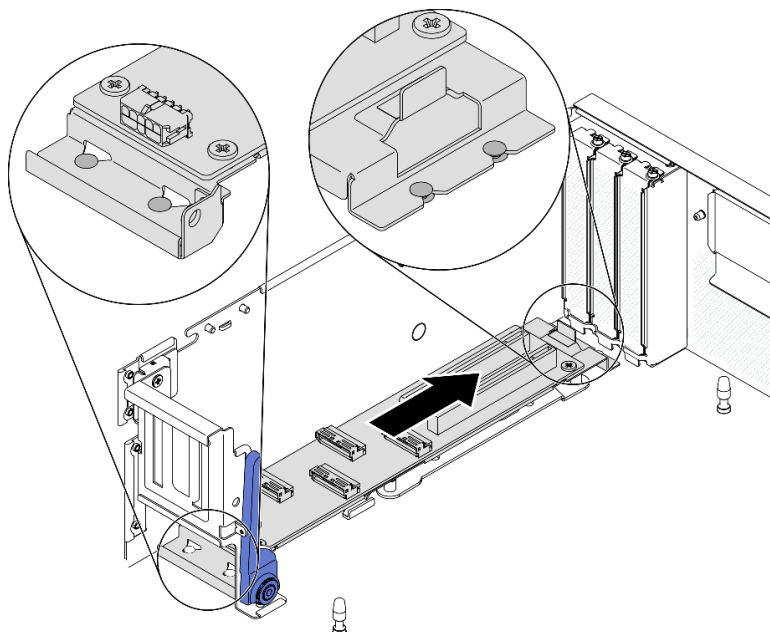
Instalando o módulo de placa de expansão de E/S frontal
